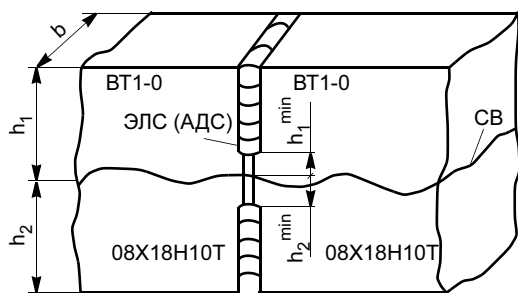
Схема стыкового соединения биметаллических титаностальных полос, выполненного электронно-лучевой или аргодуговой сваркой
